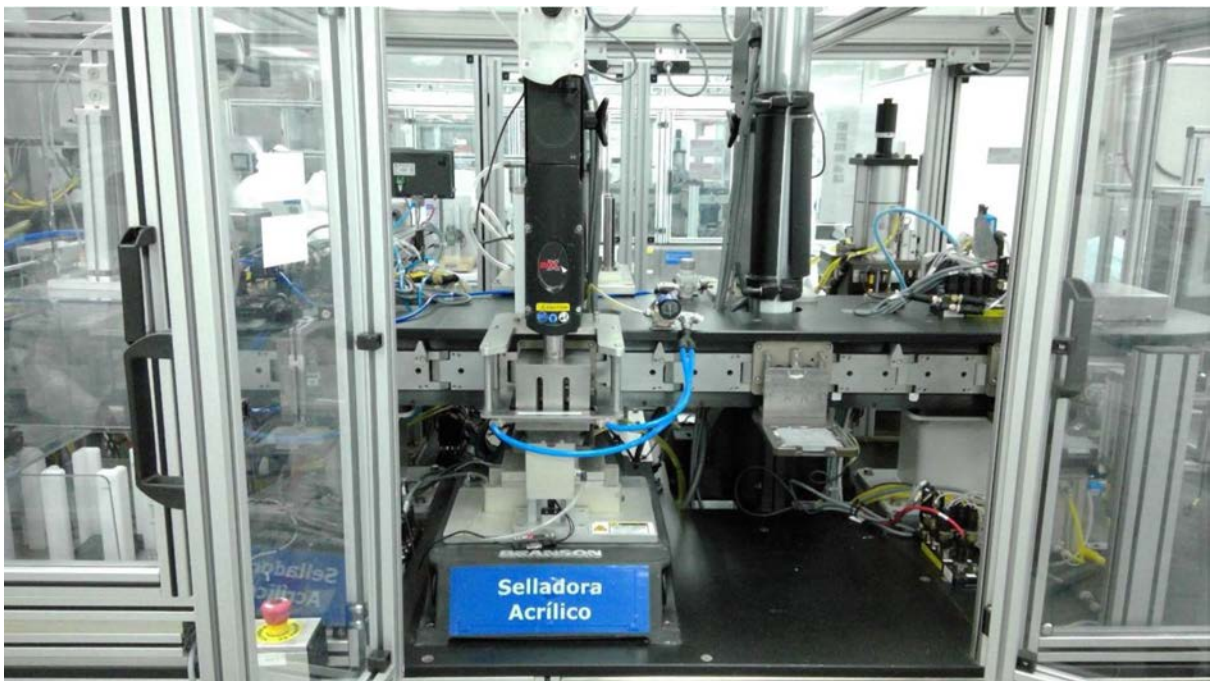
Selladora por ultrasonido en la welder automática Fresenius Kabi, Haina
